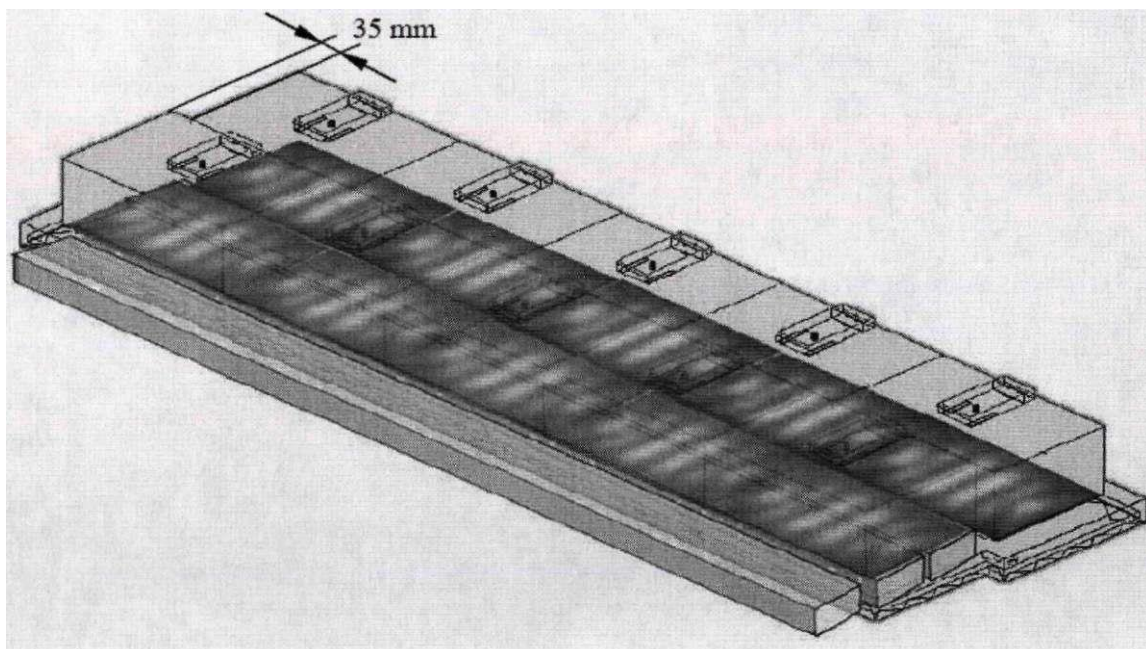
Конструкція тунелю конвеєрної СВЧ-установки для нагрівання заготовок
